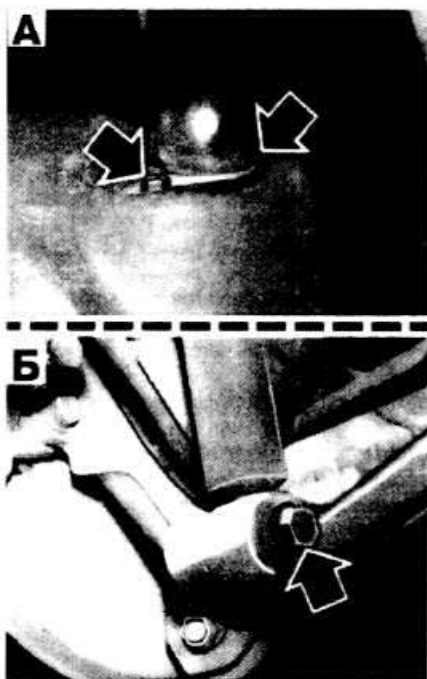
Стрелками показаны гайки крепления верхней опоры амортизатора (А) и болт нижнего крепления амортизатора (Б)
